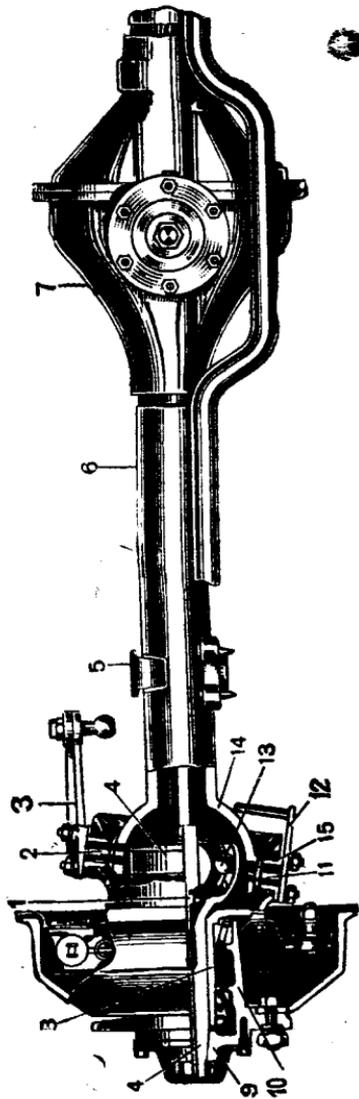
Поворотный кулак с шарниром Рцеппа:
